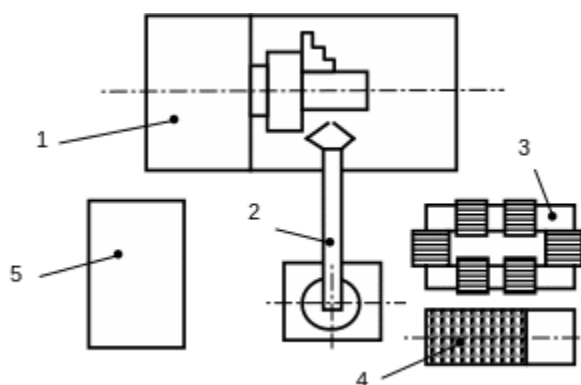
Схема ГПМ на базе токарного обрабатывающего центра: 1 – станок мод.16Б16Т1; 2 – напольный робот; 3 – накопитель заготовок и готовых деталей; 4 – инструментальный магазин; 5 – система управления ГПМ
